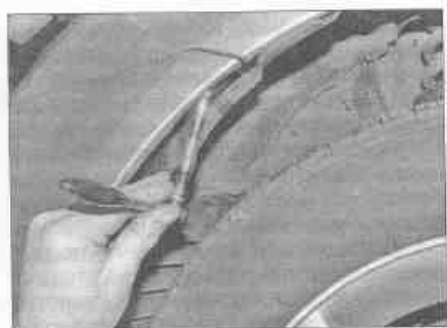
Выверните на каждой стороне болт крепления бампера к крылу
